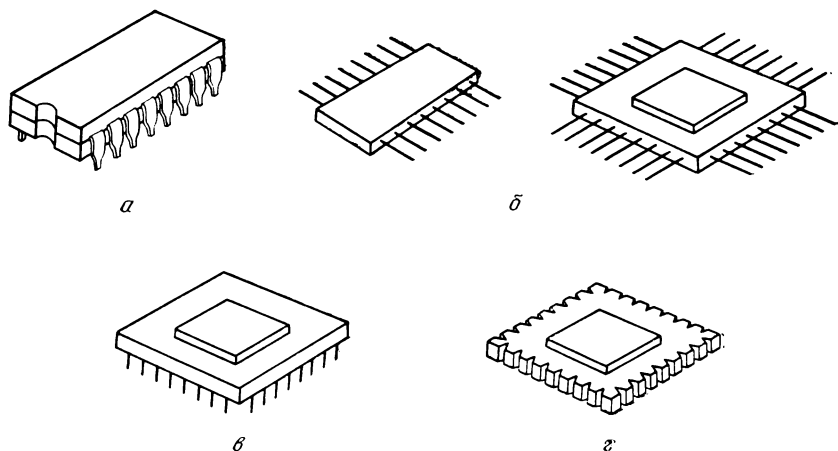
Виды корпусов ИС: *а* — двухрядный; *б* — плоский двухсторонний и плоский четырехсторонний; *в* — корпус сменной ИС со штырьковыми выводами; *г* — кристаллодержатель.
